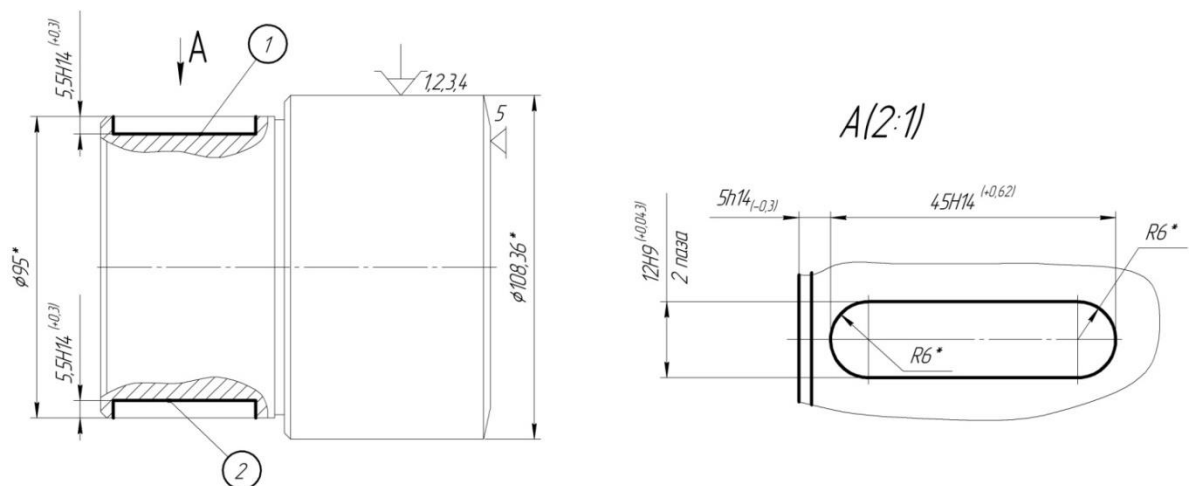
Ескіз фрезерної з ЧПК операції 030
